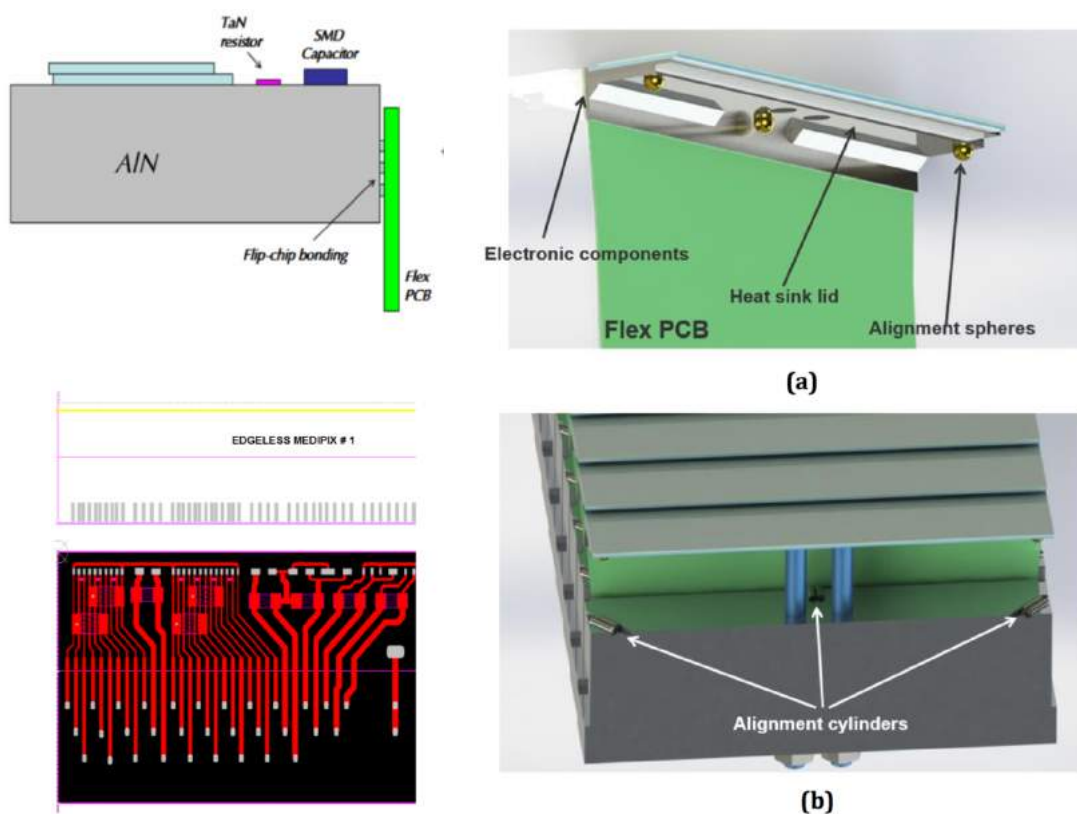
Cabeça de 6 chips com Flex PCB ligada na carrier board cerâmica. (a) Esq. Detalhe de conexão da Flex PCB. Dir: As esferas de alinhamento garantem que os 8 módulos de 6 chips se alinhem com precisão micrométrica sobre os guias magnéticos cilíndricos (b) Esq. Vias da Flex PCB e magnéticos cilíndricos que possam ser substituídos quando necessário. O contato térmico é minimizado de forma que a refrigeração trazida pelos canais (azuis) dissipe a potência dos chips (cerca de 1.5 W por chip).
